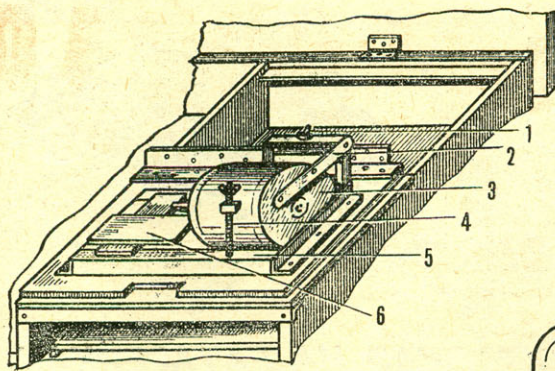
Вид тумбочки с откинутой задней половинкой крышки:
